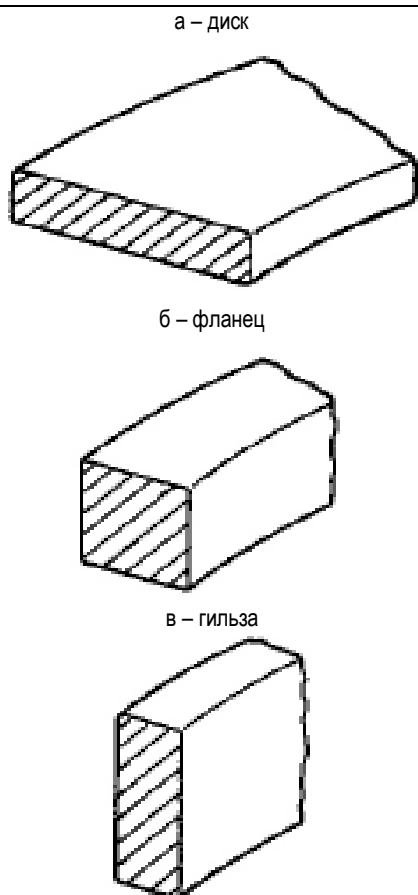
Формы деталей, изготовленных кольцераскаткой
